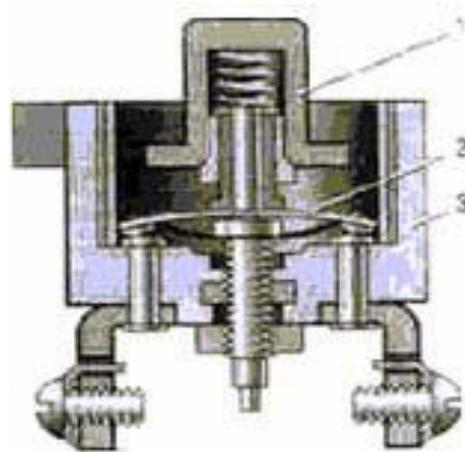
Устройство термобиметаллического предохранителя: 1 – кнопка возврата; 2 – биметаллическая пластина; 3 – корпус
